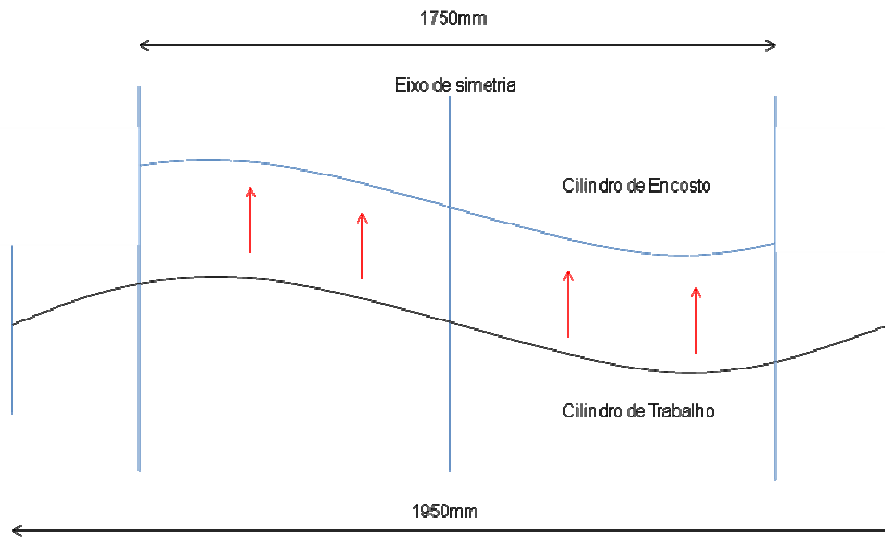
Rebatimento do perfil do cilindro de trabalho corado sobre o cilindro de encosto plano.
